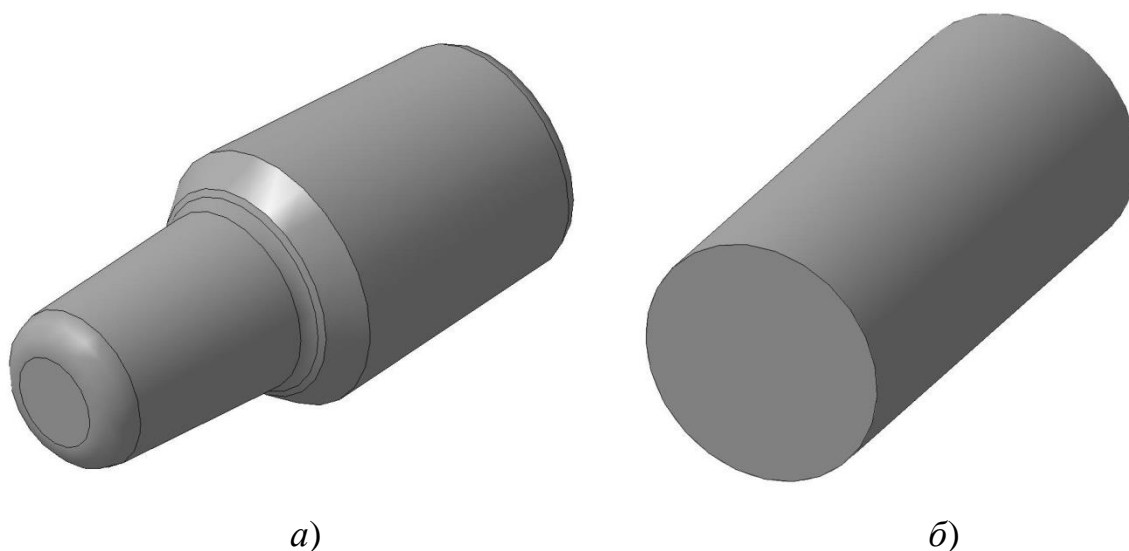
Виды заготовок: а – штамповка; б - прокат
